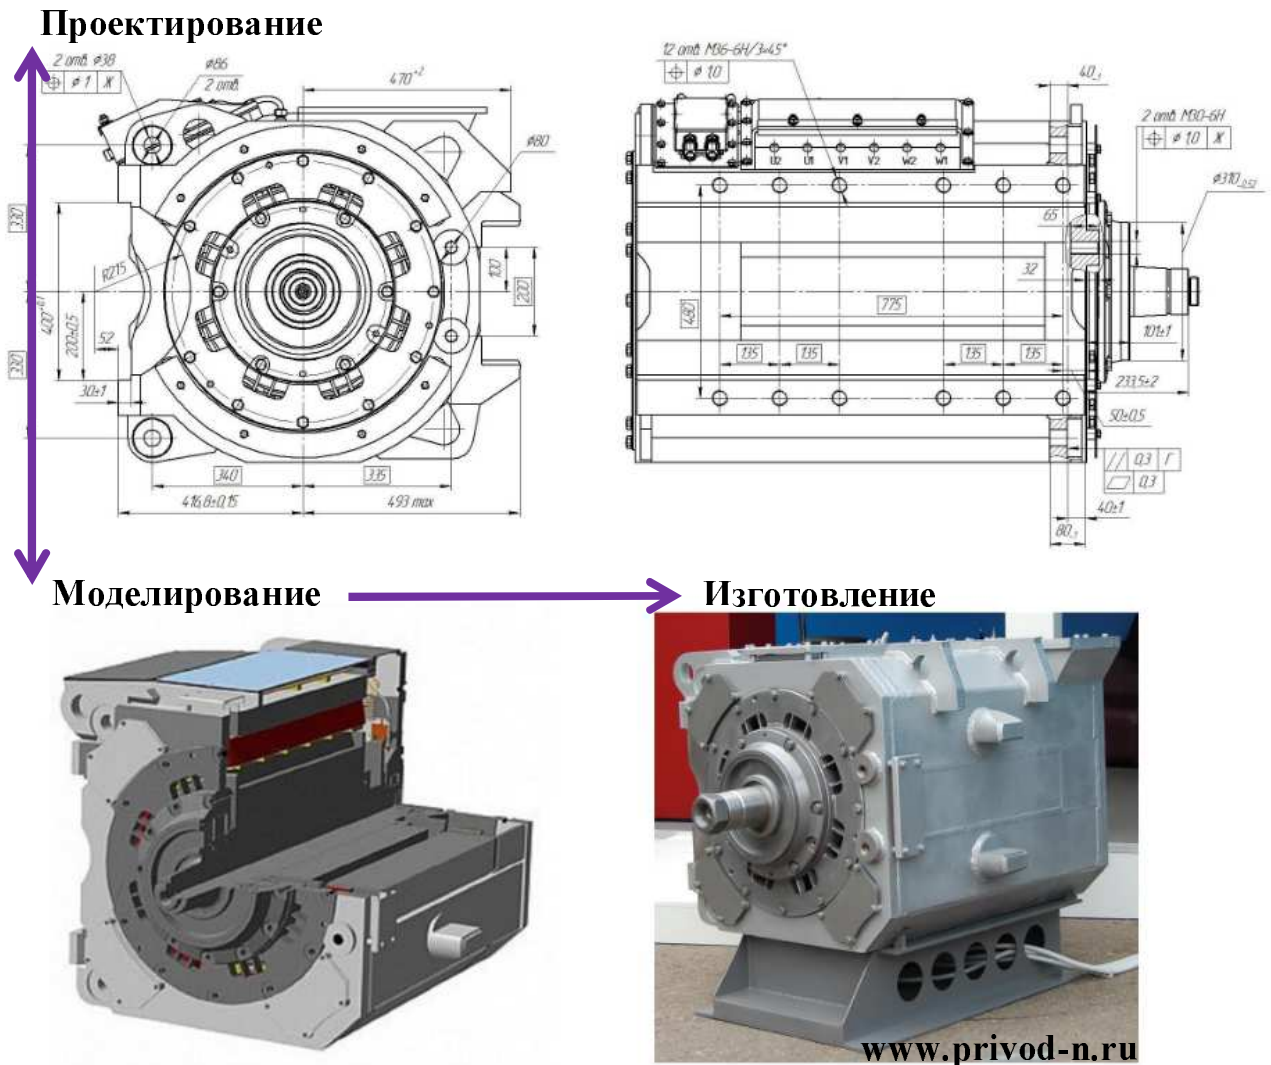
Тяговый реактивный индукторный двигатель ТРИД-125У1
